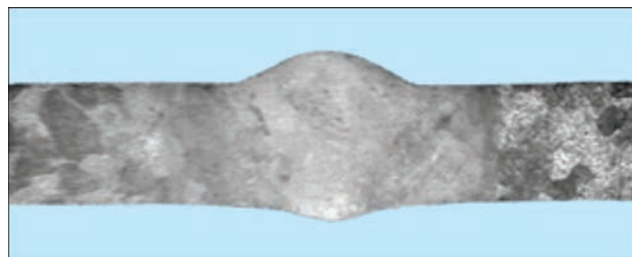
Макрошлиф сварного соединения, полученного с порошковой проволокой ППТ-22 после двухступенчатой ТО.
